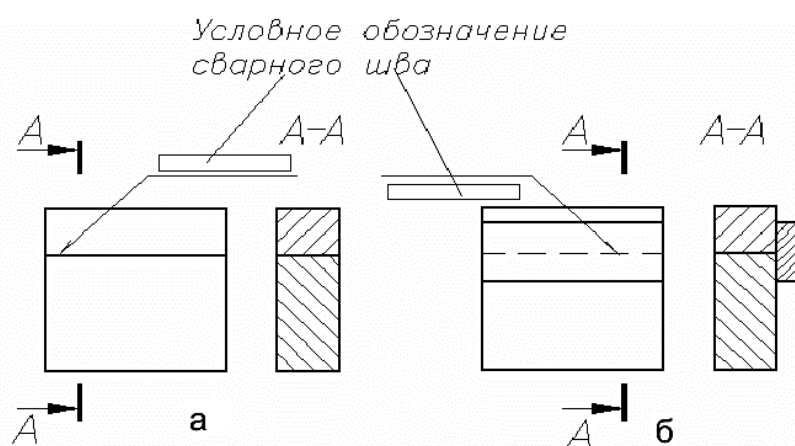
Изображение сварного шва: *а* – видимый шов; *б* – невидимый шов
